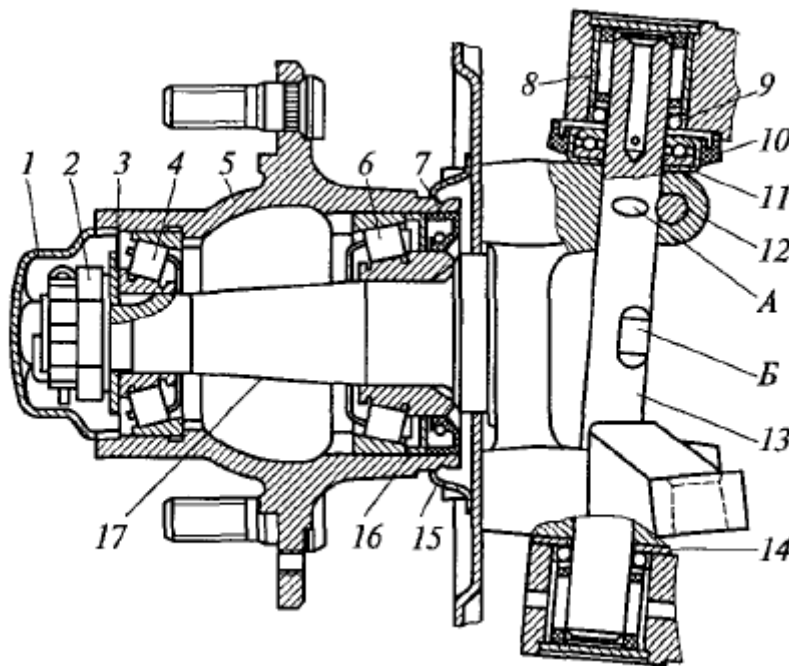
Поворотний кулак з шворнем и маточиною переднього колеса легкового автомобіля.
